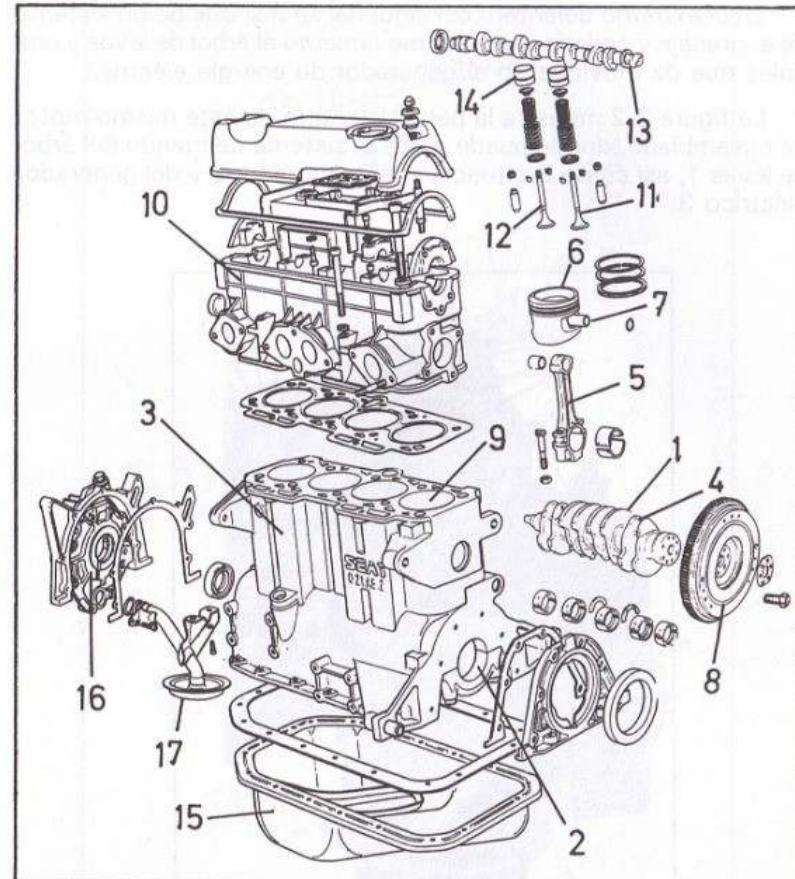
Despiece de un motor de gasolina de cuatro cilindros en línea.
